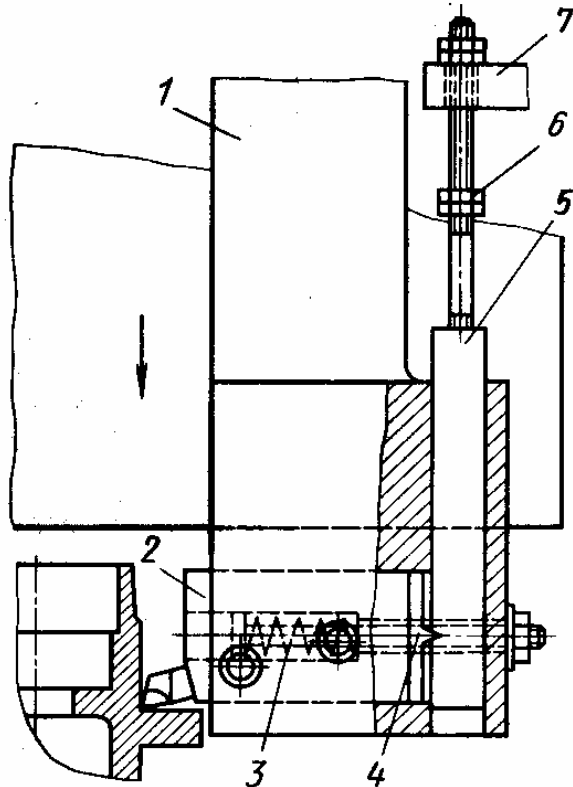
Копіювальний тримач, що забезпечує відведення інструмента від обробленої поверхні наприкінці робочого ходу
